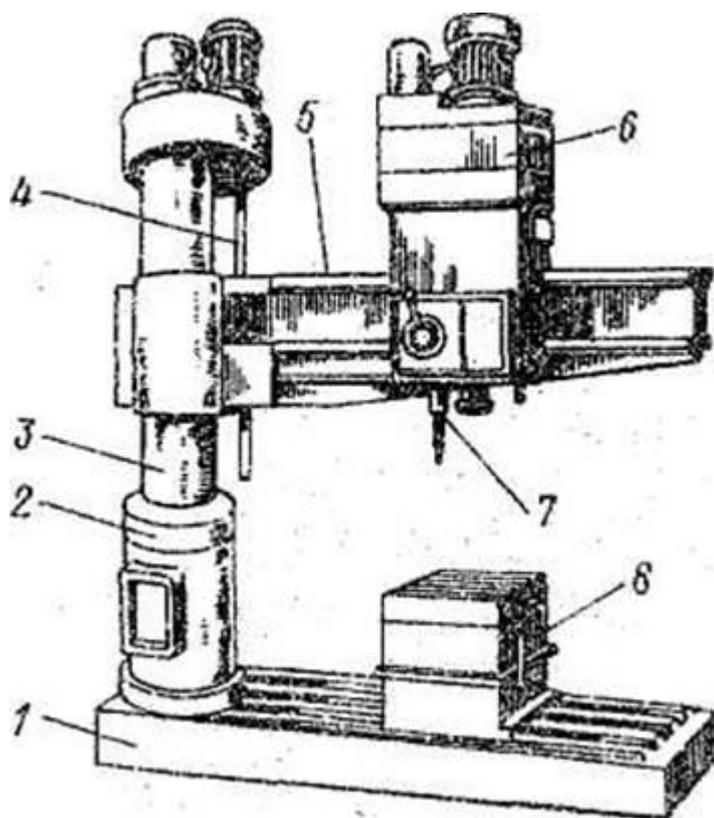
Одношпиндельный радиально-сверлильный станок общего назначения
